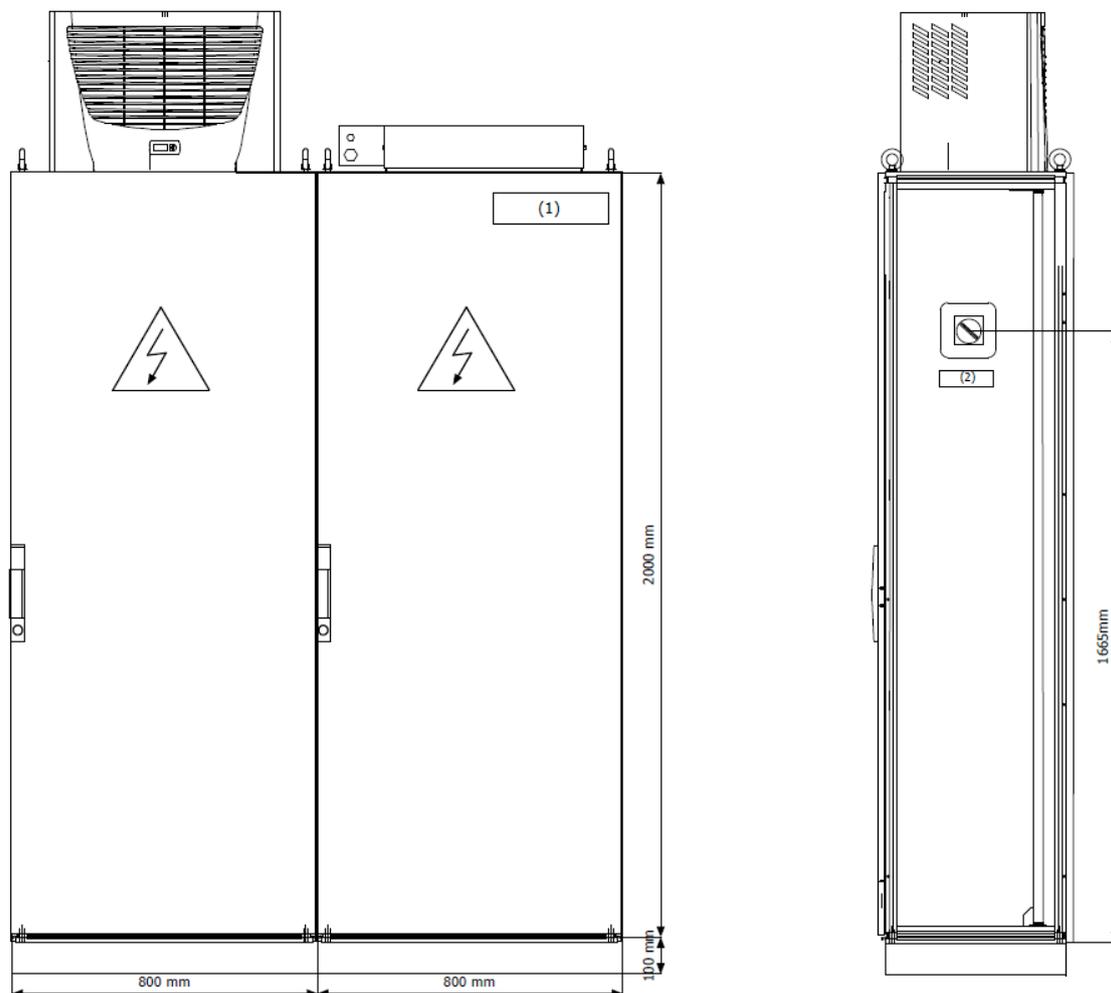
Imagen croquis exterior del armario eléctrico.
